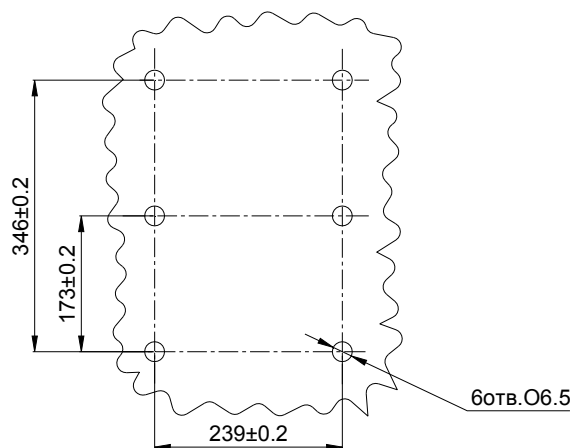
Габаритный чертеж и разметка панели под установку Блок БПД-128M4
